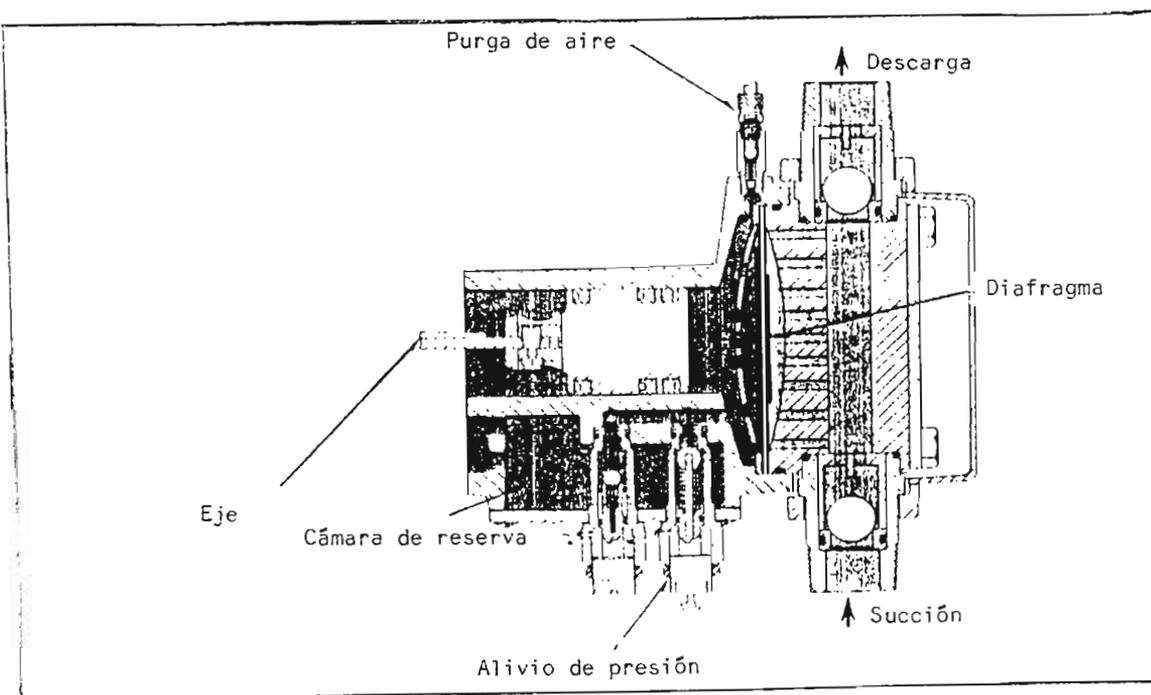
"bomba de pistón-Diafragma" (9)
